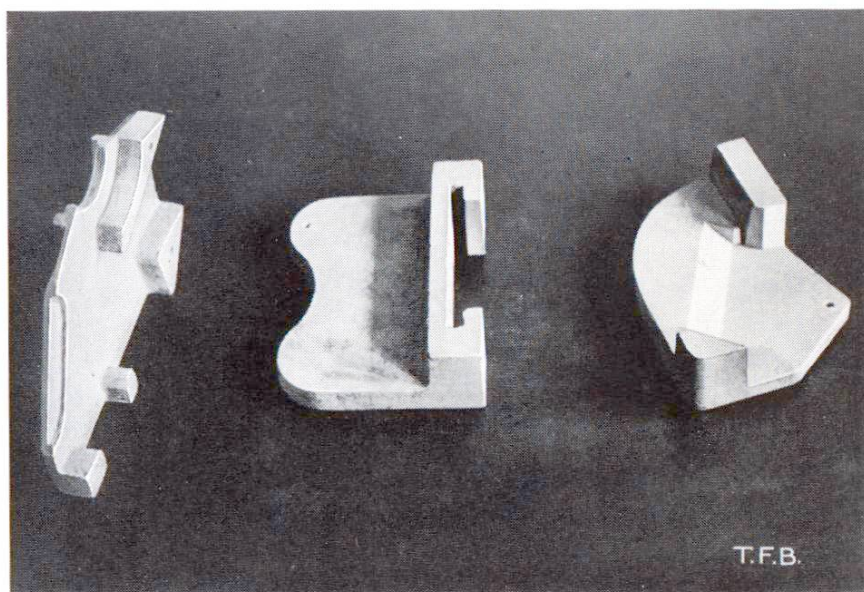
Pièces pressées en moules pour l'électro-technique, imprégnées
